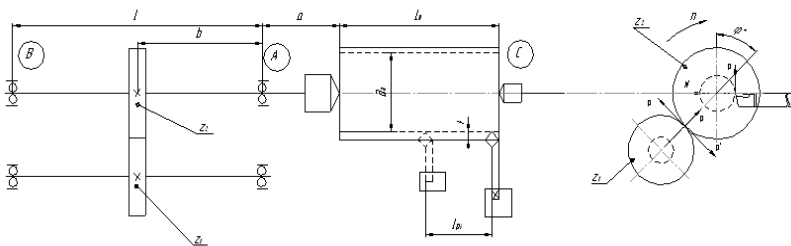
Розрахункова схема оброблення деталі на токарському верстаті з ЧПК
